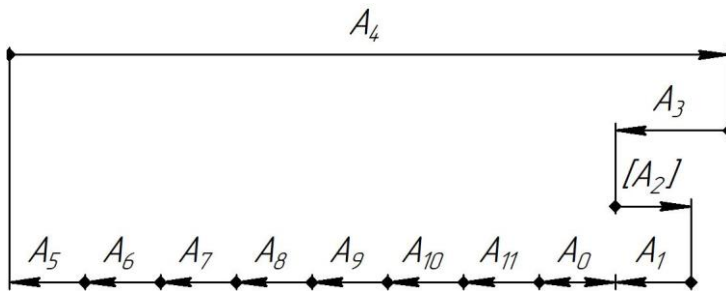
Розмірний ланцюг механізму повертання
